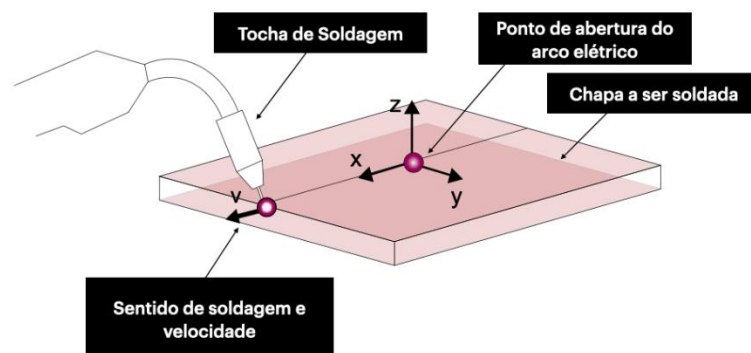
Problema físico – Soldagem a arco elétrico MIG/MAG
